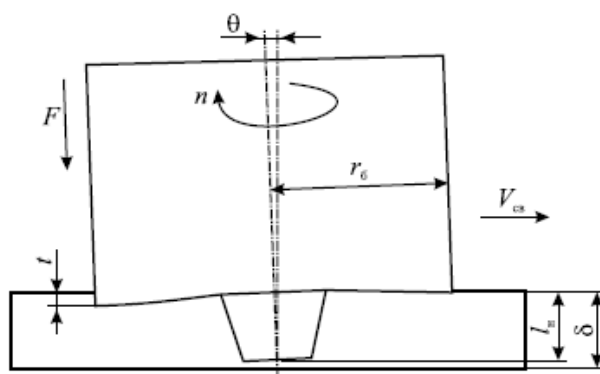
Основные параметры сварки трением с перемешиванием [25].
